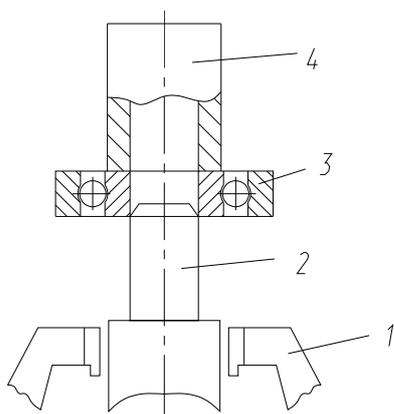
Схема опытной установки для напрессовки подшипника на вал
